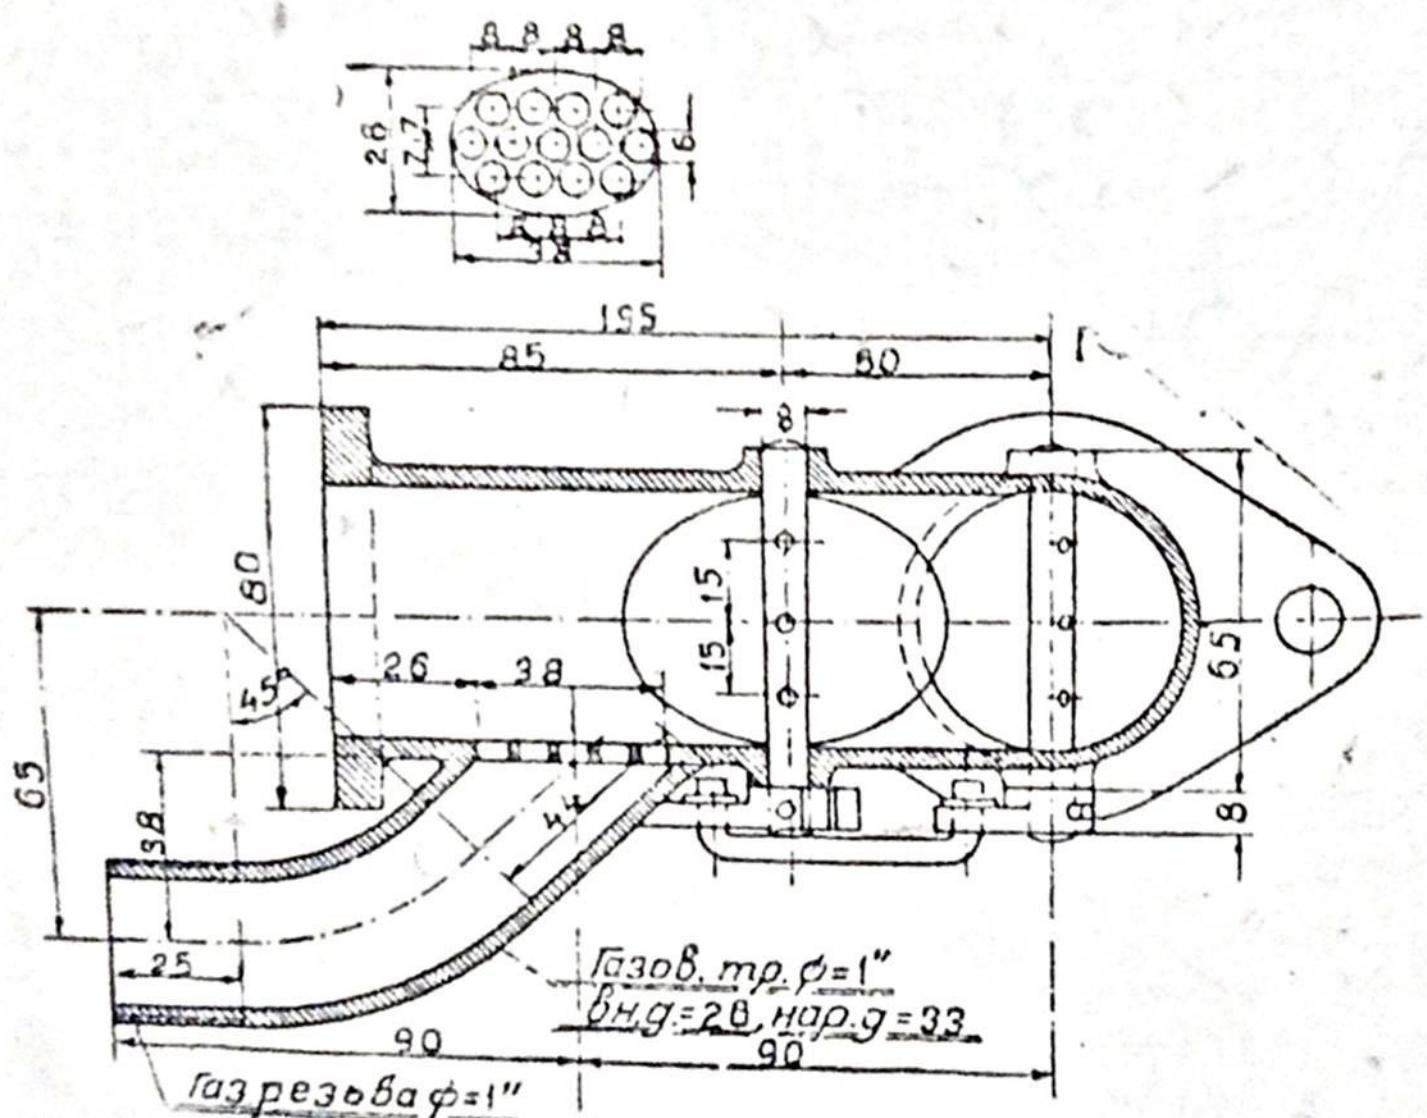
а. Смеситель газа и воздуха для двигателя 50-75 А. С.
